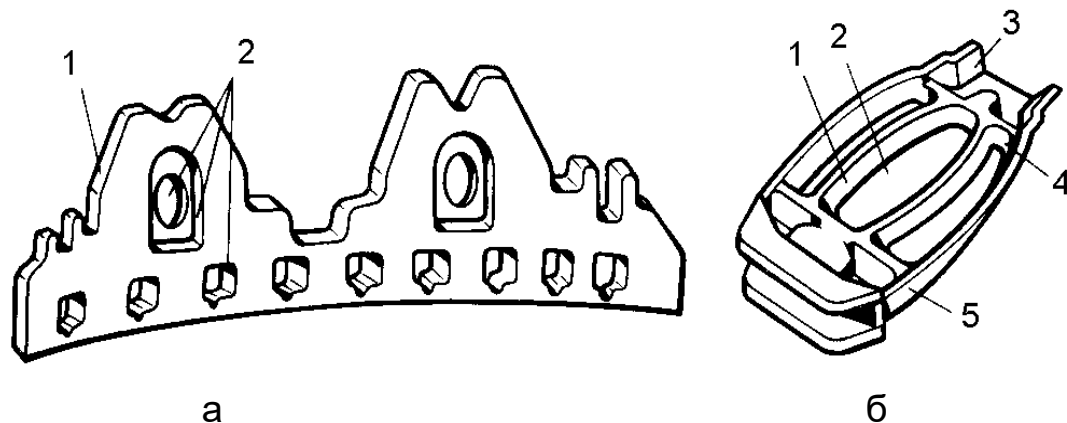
Типовые детали силового набора крыла, обрабатываемые на пятикоординатных станках с ЧПУ
